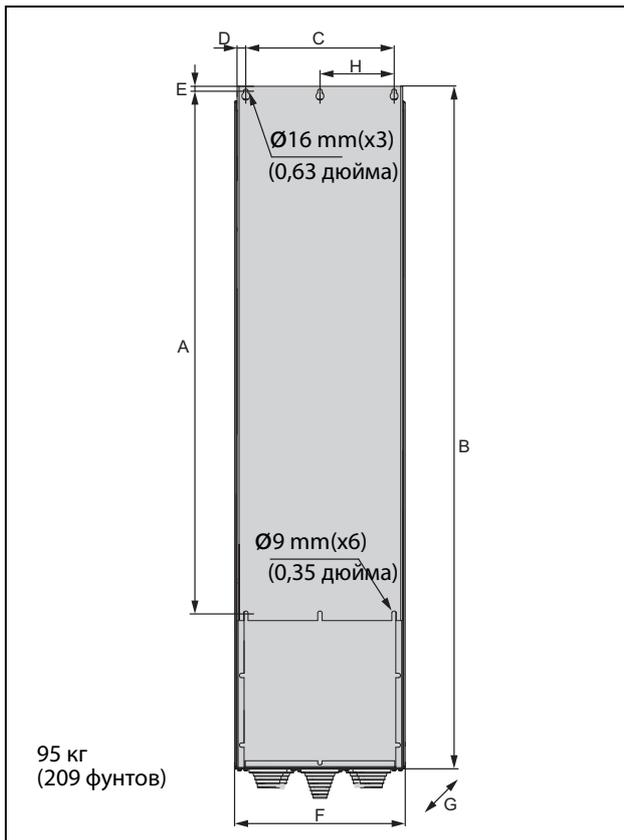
Устройство Emotron FDU модели 48-365-54 (размер корпуса FA).
